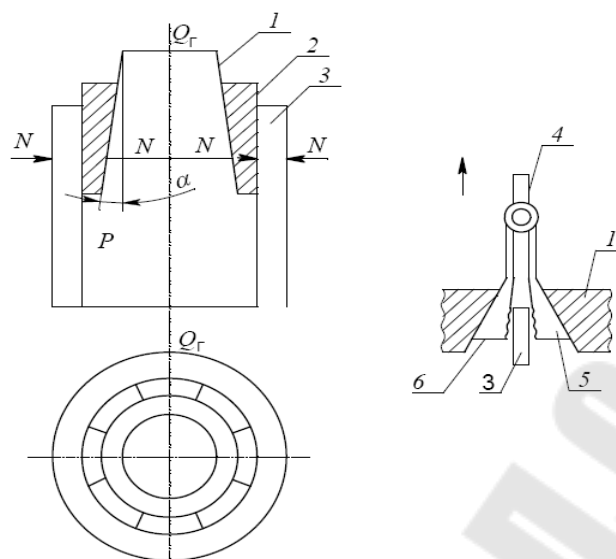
Схемы рычажно-клинового ЗУ: 1- конусообразный клин; 2 - конический сегмент; 3 - деталь; 4 - подъемное звено; 5, 6 - распорные элементы
